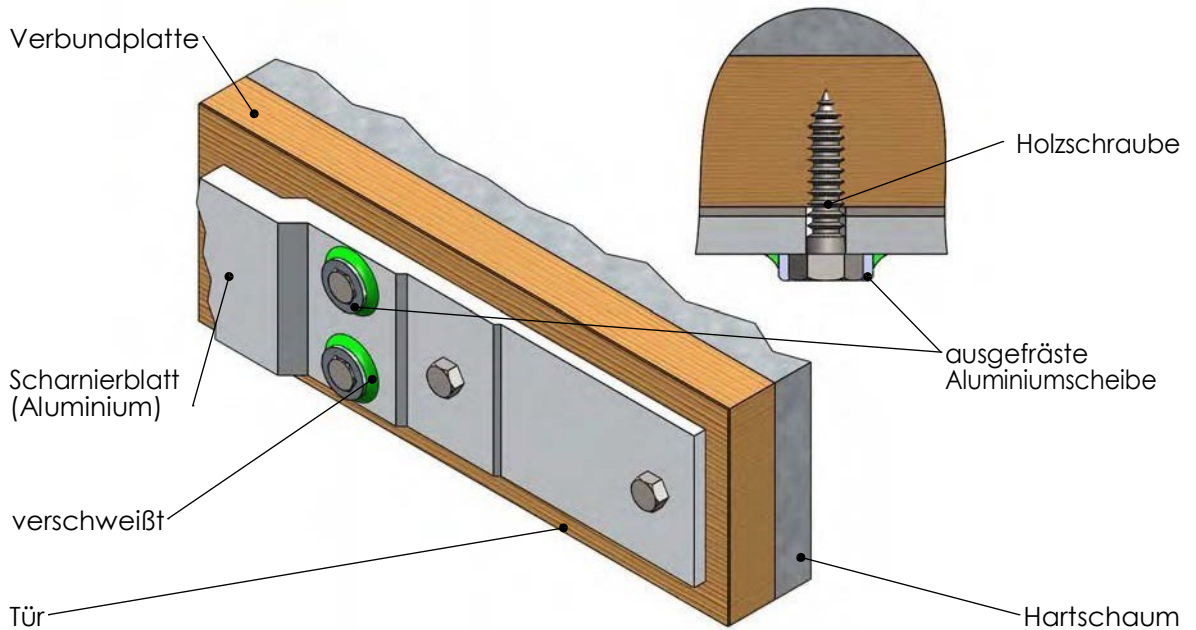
Sicherung mit ausgefrästen Aluminiumscheiben
